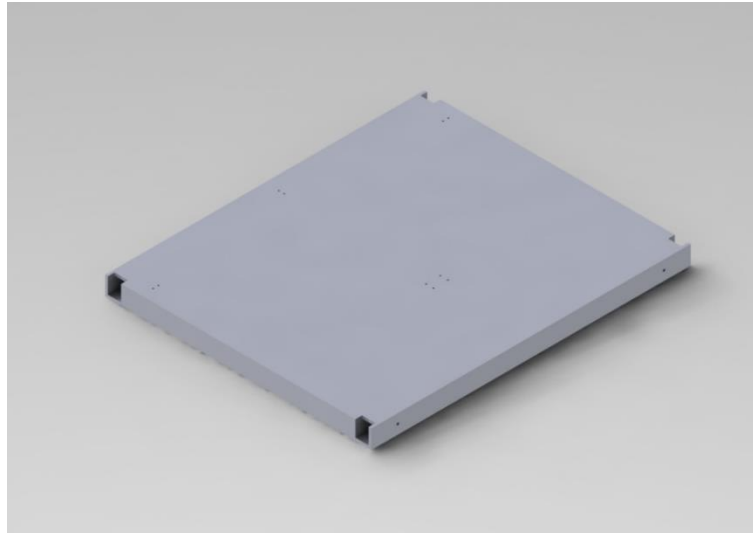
Ensamblaje subconjunto 1.3. Soldadura 37, 38, 39 y 40
